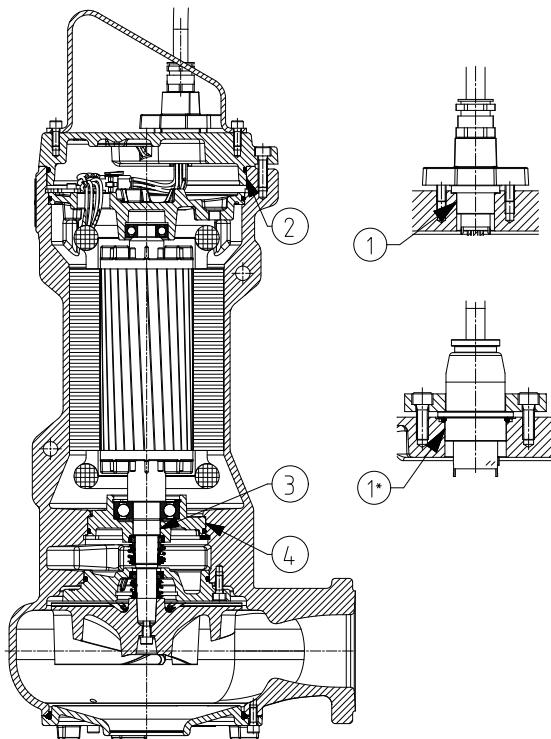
Обзор поверхностей взрывозащитных зазоров
